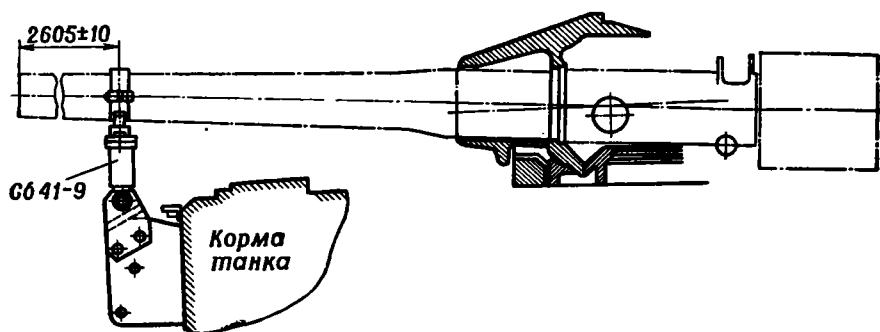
Установка приспособления (С6.41-9) для проверки фрикциона сдающего звена подъемного механизма
